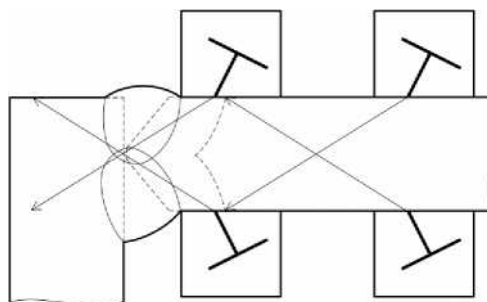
Схема контроля угловых сварных соединений прямыми лучами.
